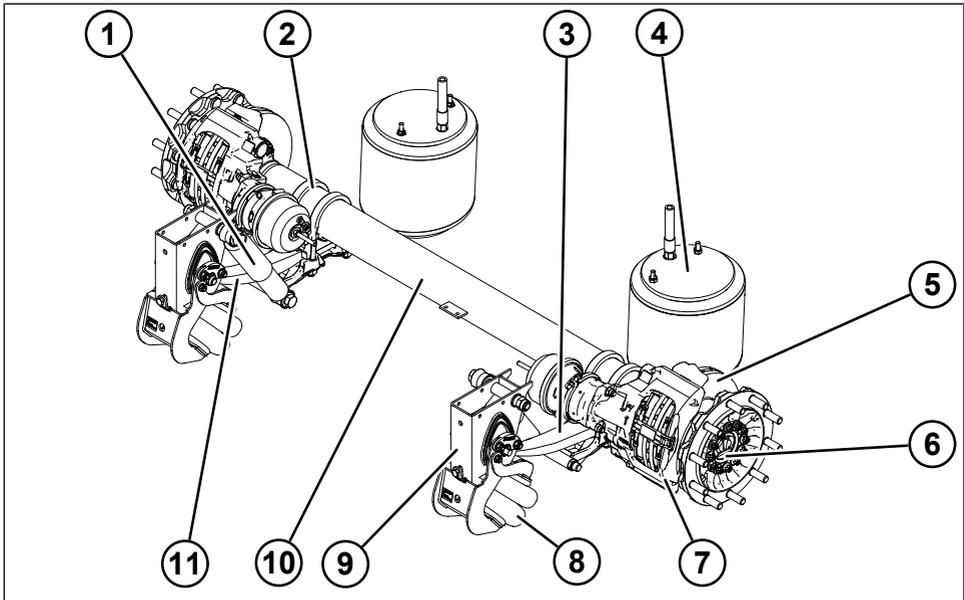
Baugruppen der KRONE Trailer Achse (Luftfederlenker unten)
